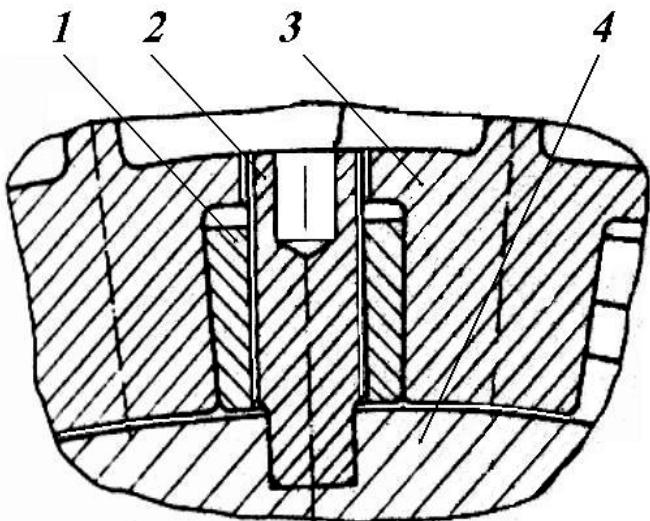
Фиксация рабочих лопаток компрессора IV – XII ступени:
